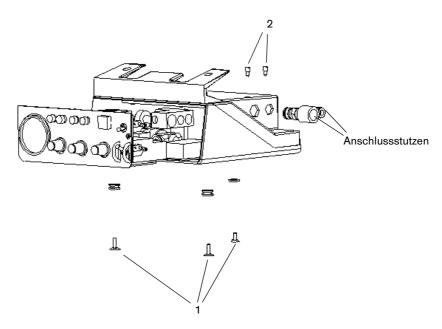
Ansicht auf das Oxylog 1000, Schrauben entfernen
